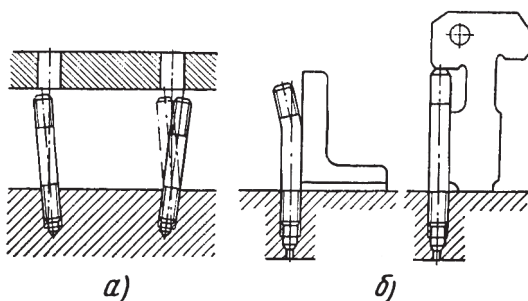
Контроль установки резьбовых шпилек в деталь
